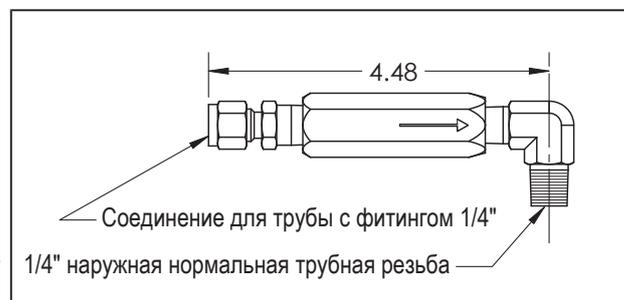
Угловой двойной обратный клапан для точек смазки компрессора.
